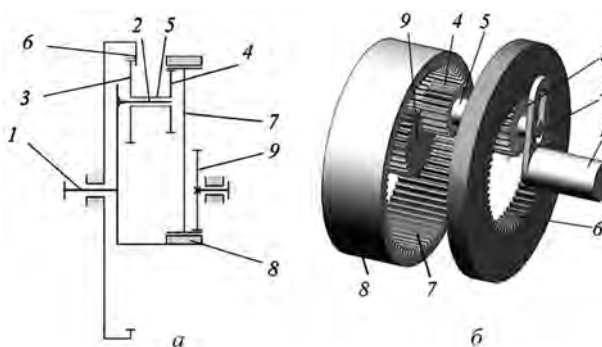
Модель вариатор-редуктора: *a* – кинематическая схема; *б* – модель; 1 – ведущий вал; 2 – кривошип; 3 – сателлит; 4 – дополнительный зубчатый венец сателлита; 5 – втулка; 6 – центральное зубчатое колесо; 7 – вспомогательный зубчатый венец; 8 – обойма; 9 – выходное зубчатое колесо
